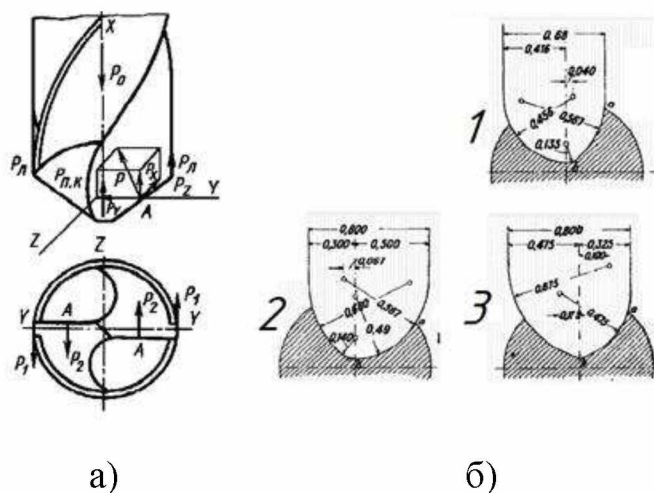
Схема сил, що діють на ріжучу кромку свердла: а – схема сил, що діють на свердло; б – геометрія робочої поверхні ріжучої кромки гвинтової канавки свердла
